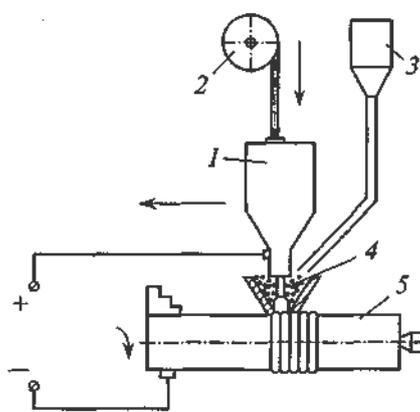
Схема автоматической дуговой наплавки цилиндрических деталей под флюсом:
